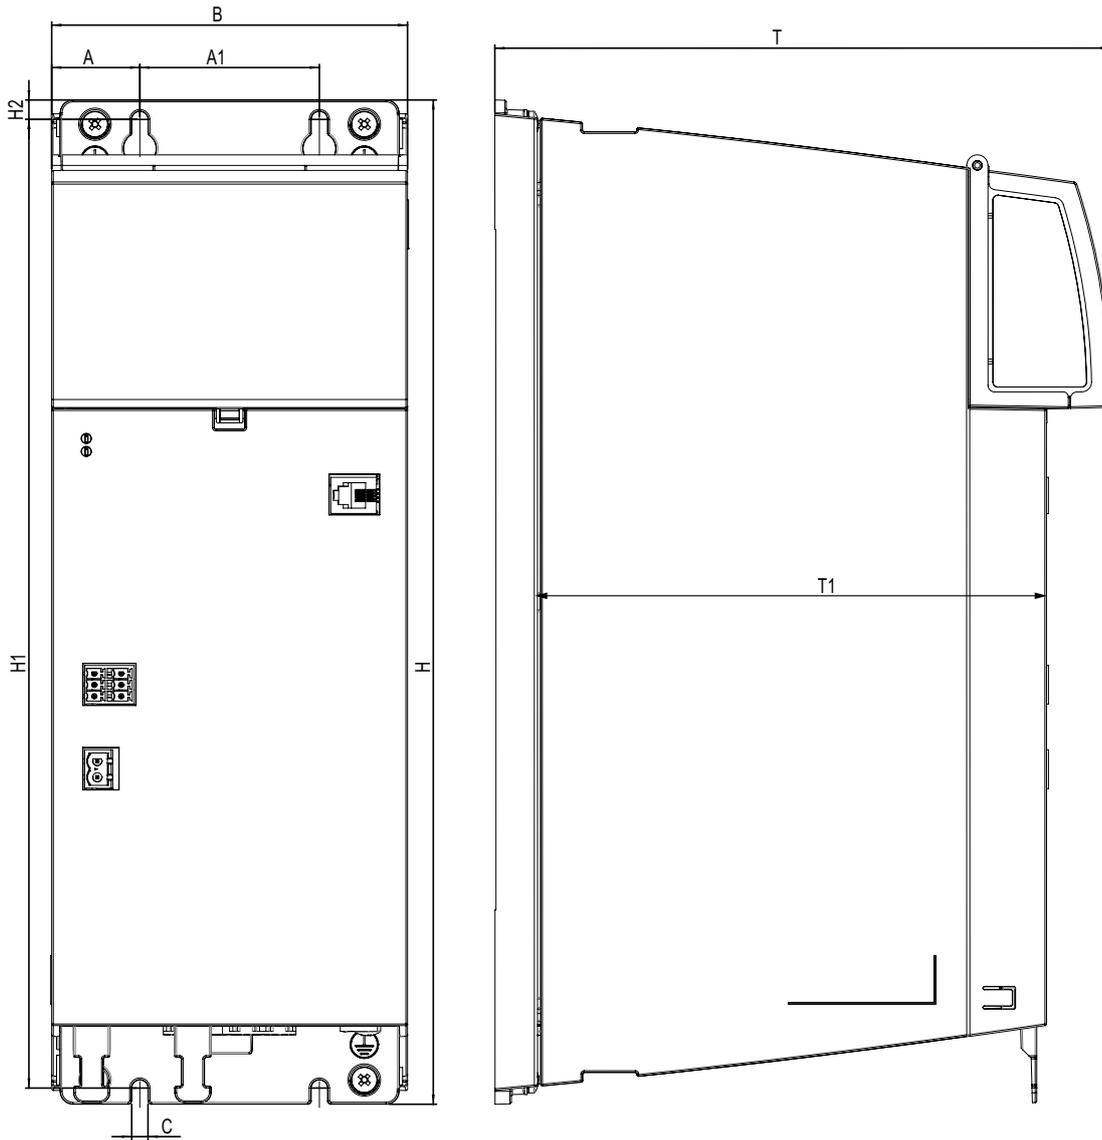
JM-3000 电源装置 BG2 冷却板尺寸图（尺寸请参见表表 2.2）
